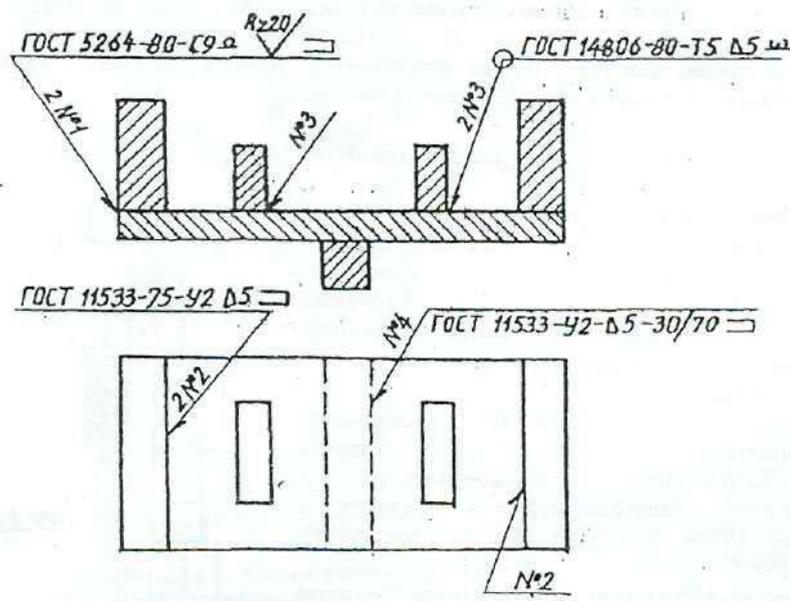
Условное обозначение сварных соединений
